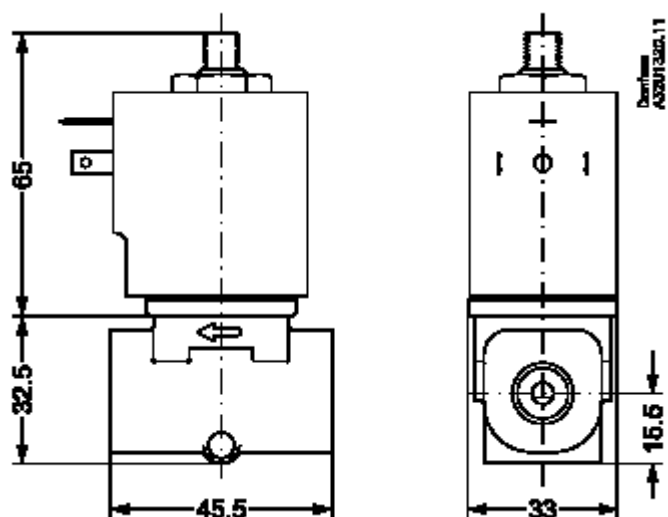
Габаритные и присоединительные размеры клапана с резьбовым присоединением.
